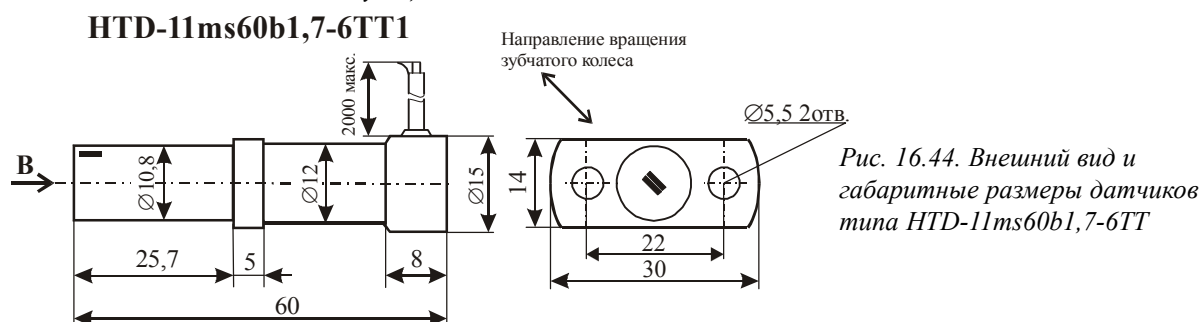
Внешний вид и габаритные размеры датчиков типа HTD-11ms60b1,7-6TT
